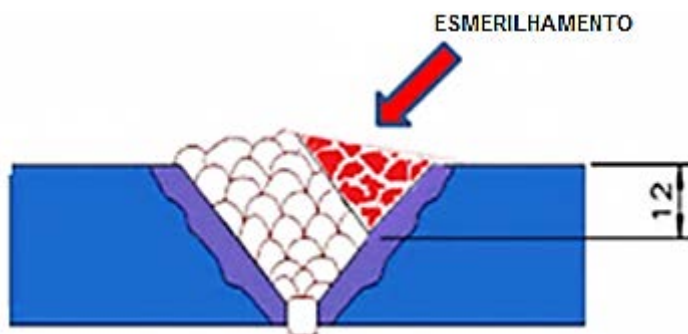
Junta soldada com a remoção da última camada de solda.
